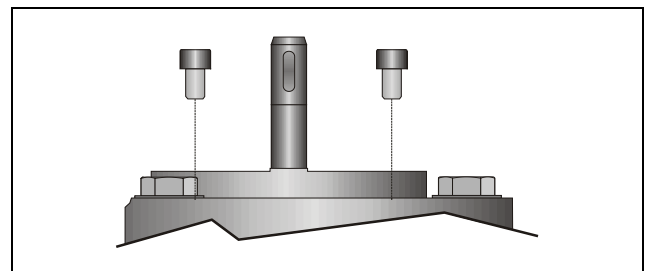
Soltar y quitar los tornillos de cabeza cilíndrica
